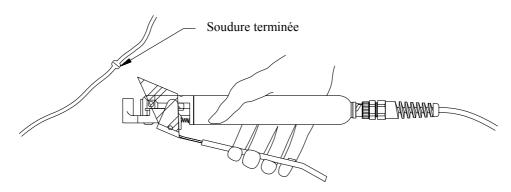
Relâchement du levier de la tête de soudure après la fin de la soudure
